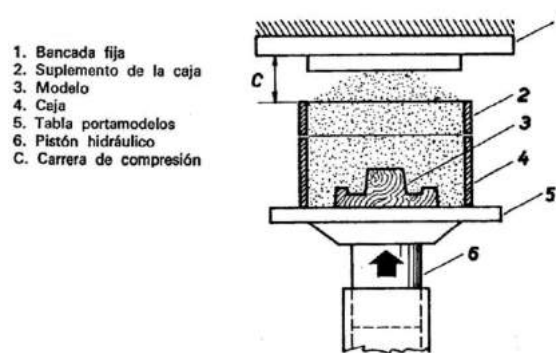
Moldeado por presión. (Fuente: Apuntes Fundición ICAI)
